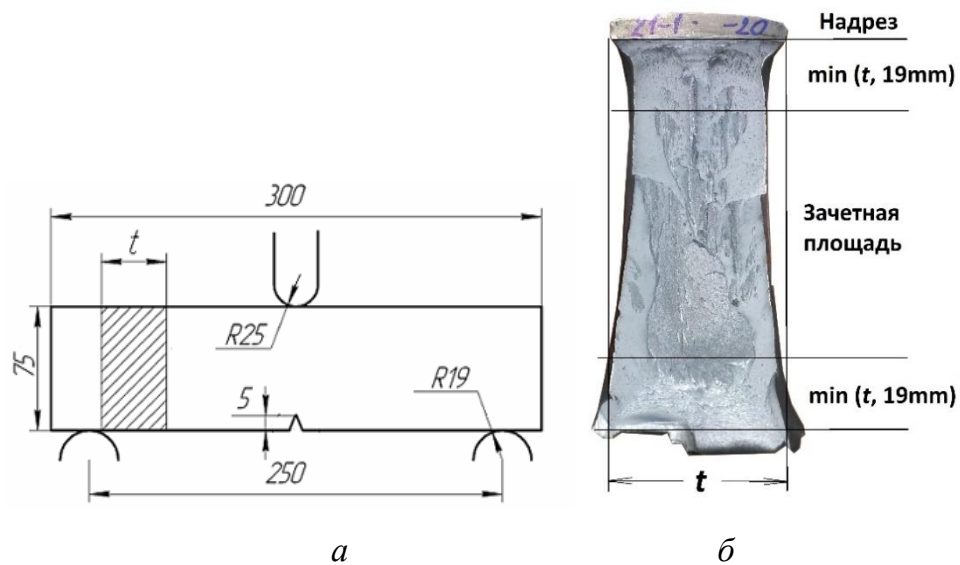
Схема испытаний и образца ИППГ –а и схема оценки вида излома –б.
